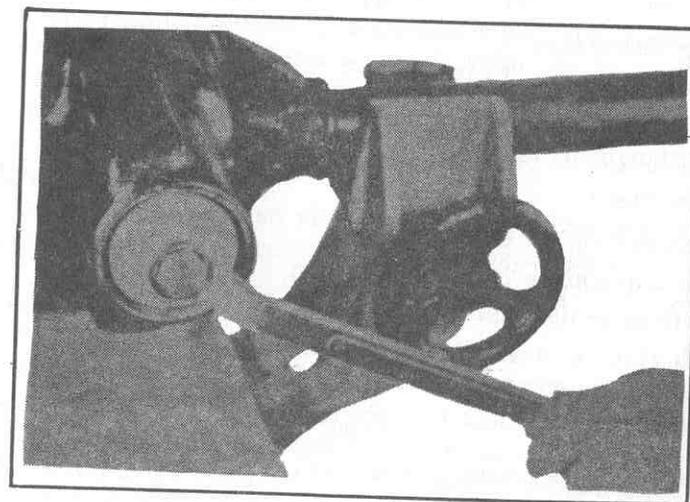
Montaje de la cubeta del cojinete trasero.
